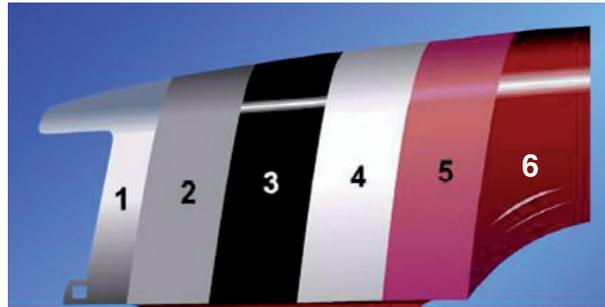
Aufbau der Beschichtung einer Fahrzeugkarosserie
